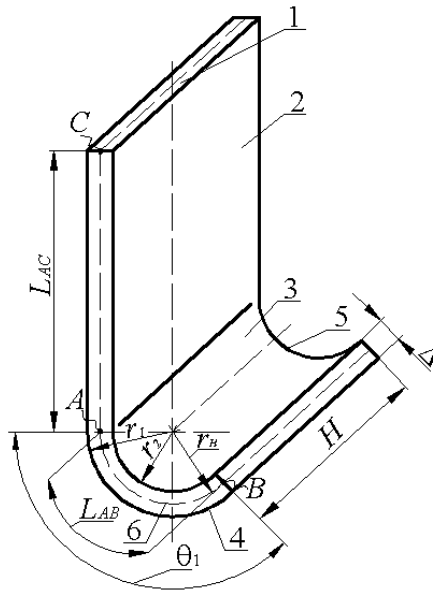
Схематичне зображення заготовки згортної втулки з плоско-циліндричними ділянками
